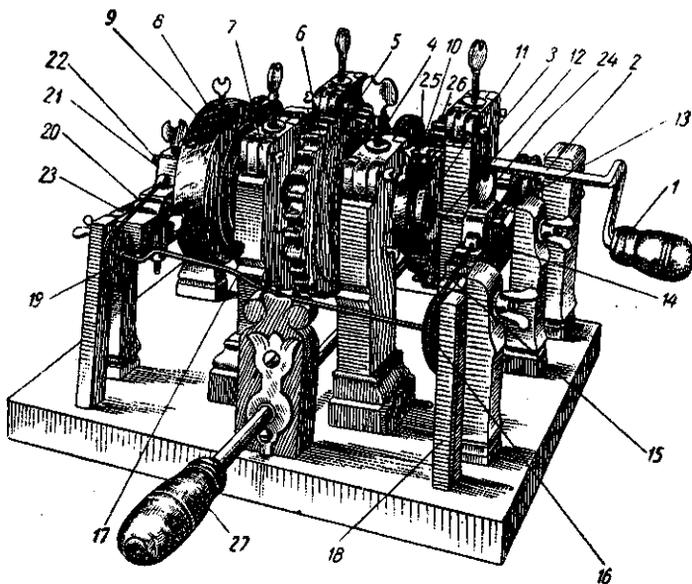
Кинематическая схема токарно-копировального станка Е. Блеера.
